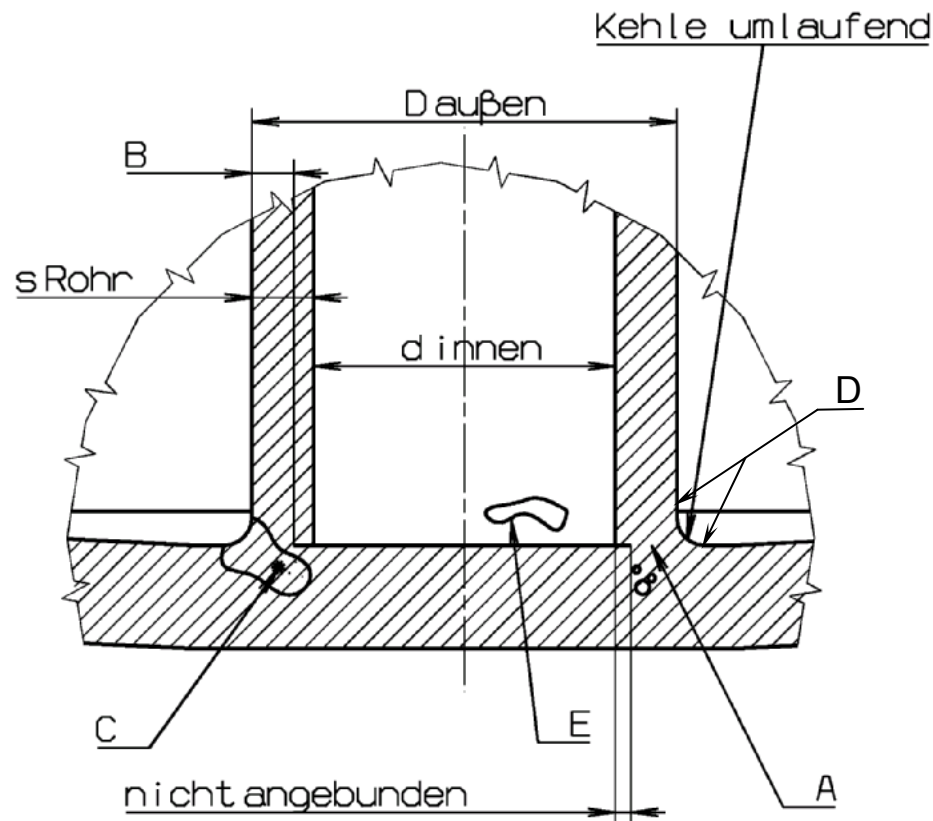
ZB1; Schweißdefinitionen Teller/Rohr
